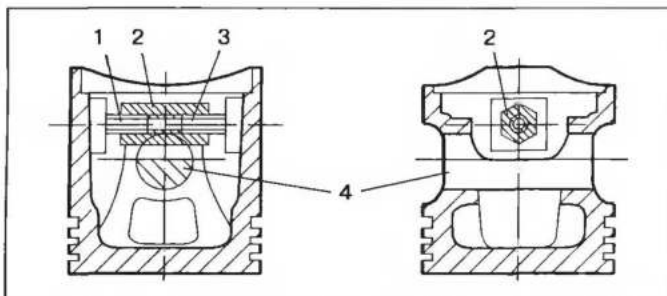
Схема простейшего приспособления для "растягивания" деформированной юбки поршня:
